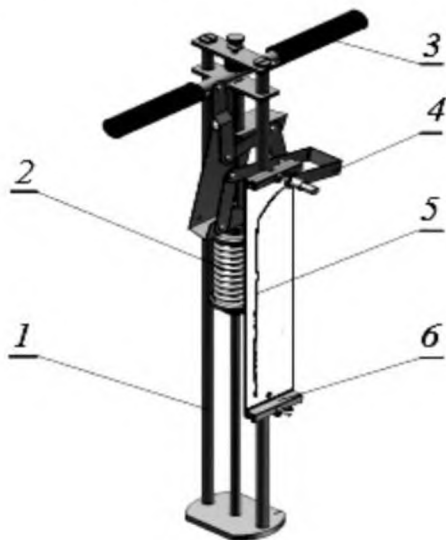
Загальний вигляд твердоміра Ю. Ю. Ревякіна: 1 – штанга напрямна; 2 – пружина; 3 – рукоятка; 4 - пристрій записуючий; 5 – діаграма; 6 – планка для паперу; 7 – штанга телескопічна; 8 – основа; 9 – наконечники змінні
